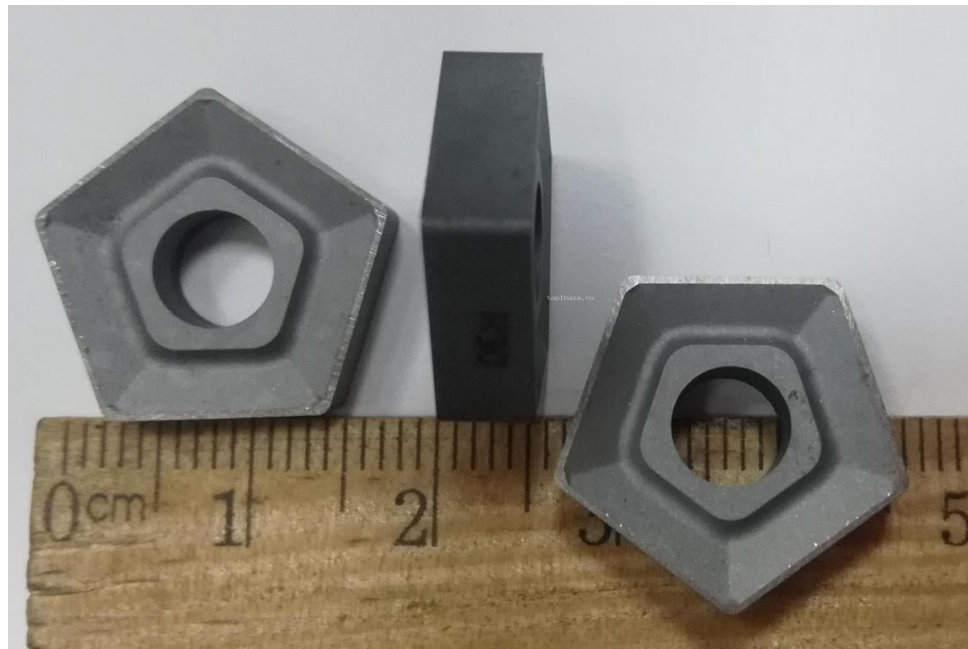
Твердосплавні пластини для механічного кріплення
